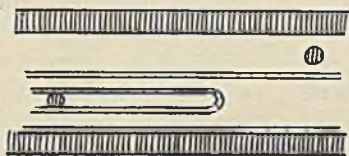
Verschweißen von 3 Blättern zu einem Hohlkörper mit Drahtstanzen
